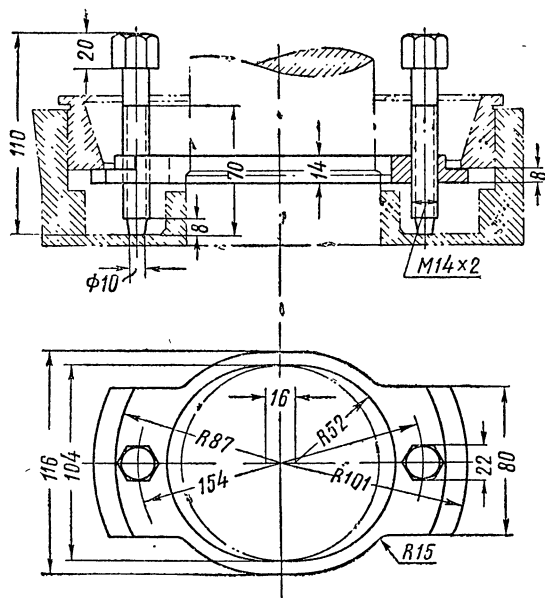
Съемник для снятия наружного кольца внутреннего роликоподшипника ступицы.
